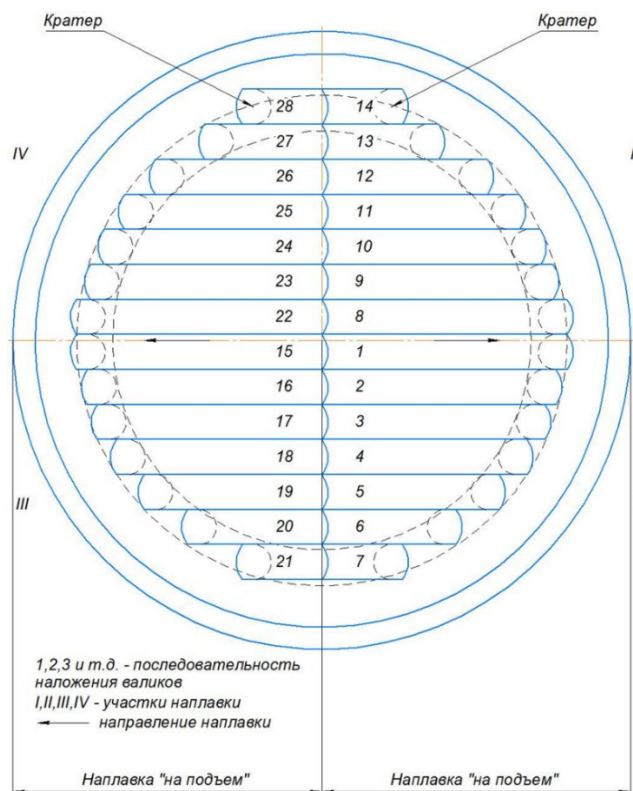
Схема наплавки центра внутренней поверхности дна ёмкости
